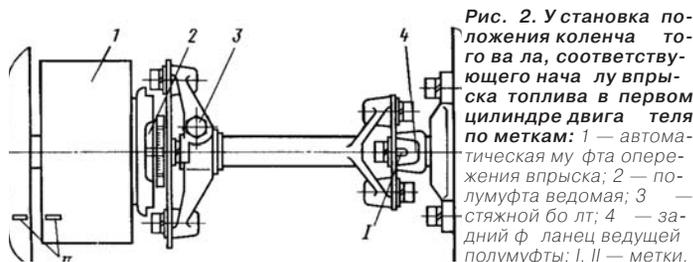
Установка положения коленчатого вала, соответствующего началу впрыска топлива в первом цилиндре двигателя по меткам: 1 — автоматическая муфта опережения впрыска; 2 — полу-муфта ведомая; 3 — стяжной болт; 4 — задний фланец ведущей полу-муфты; I, II — метки.
